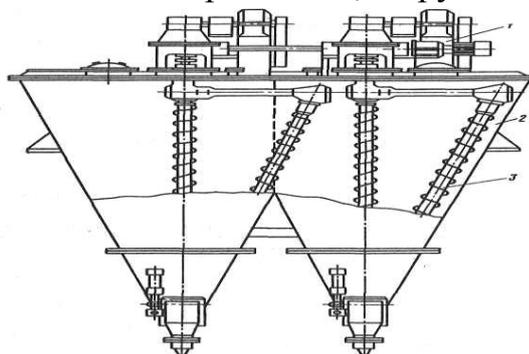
Планетарно-червячный смеситель: 1-привод, 2-конический корпус, 3-перемешивающие устройства.
